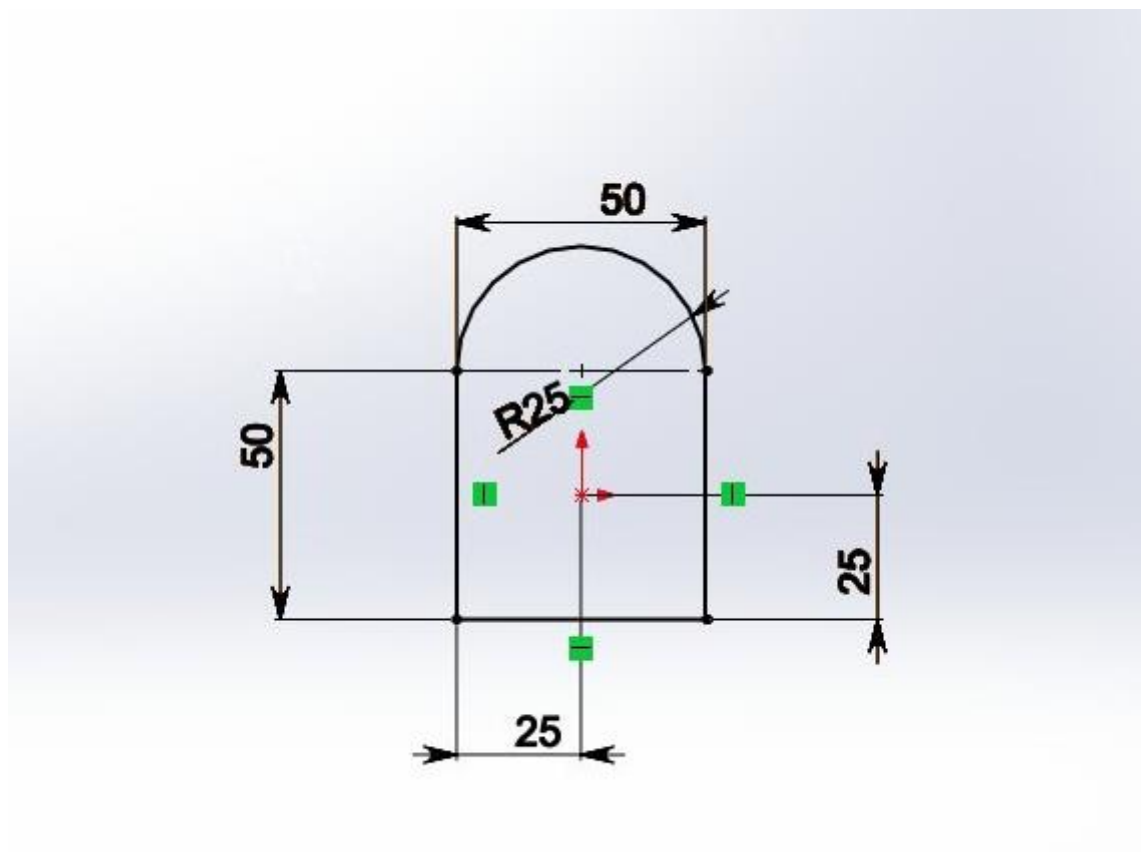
Нанесение размеров на эскиз в SolidWorks
